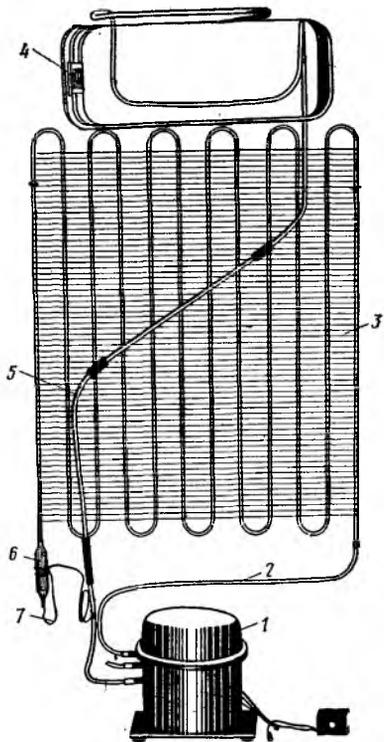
Компрессорный холодильный агрегат с одним испарителем:
